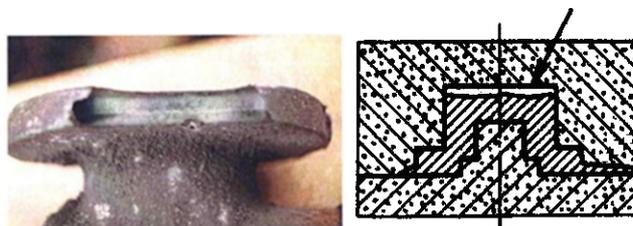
Фрагмент отливки «Корпус вентиля» с дефектом «Уход металла»
